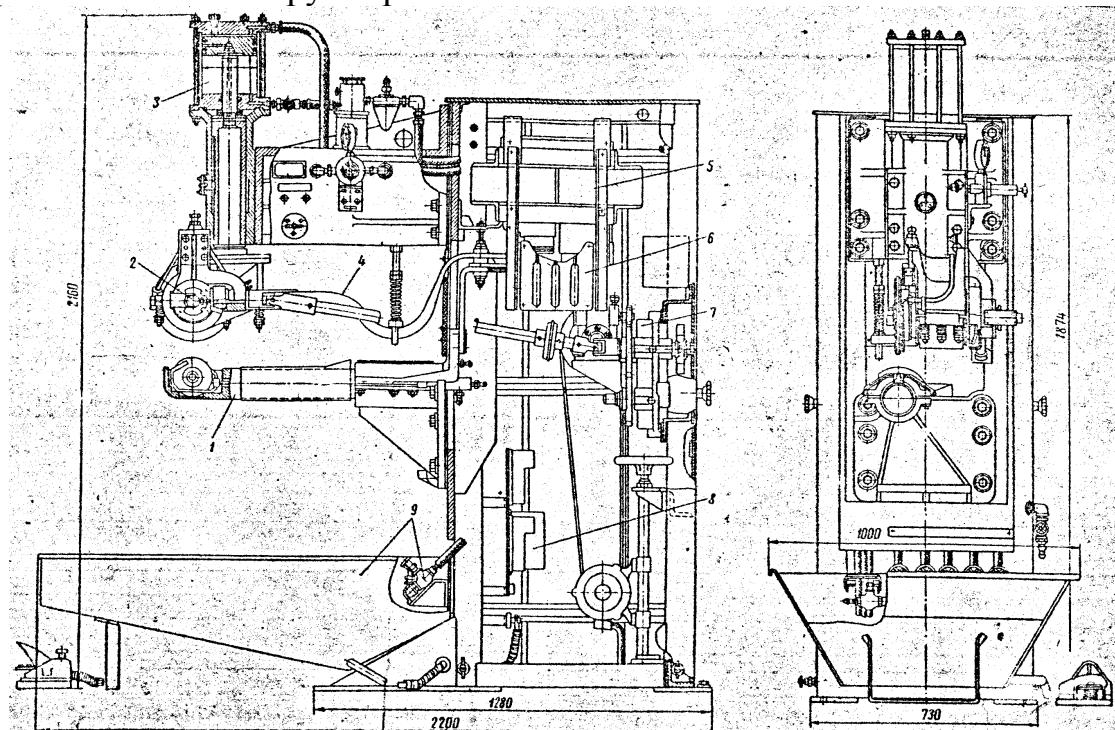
Общий вид машины шовной контактной сварки
